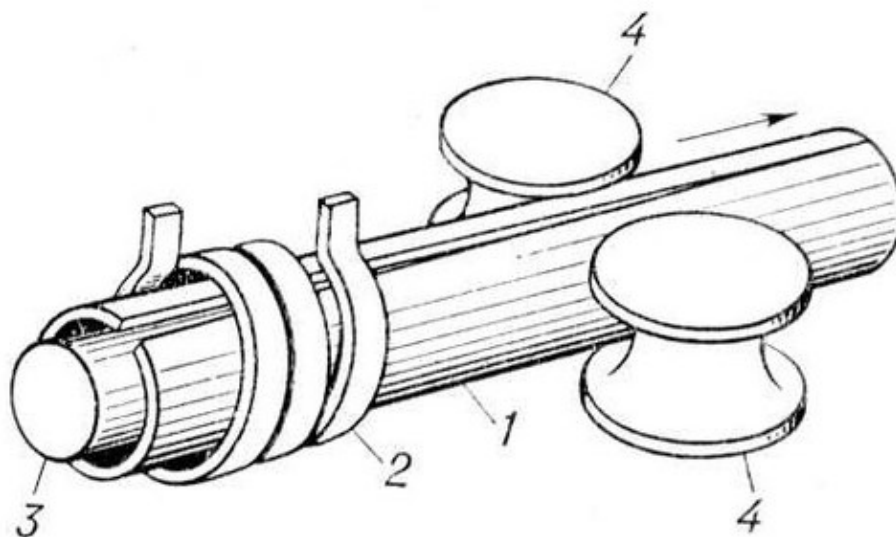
Шовная сварка трубы индукционным способом: 1 – труба; 2 – индуктор; 3 – сердечник; 4 – обжимные ролики.
